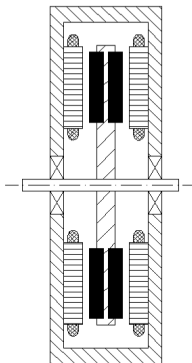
Rotor se asymetrickým magnetickým tokem
